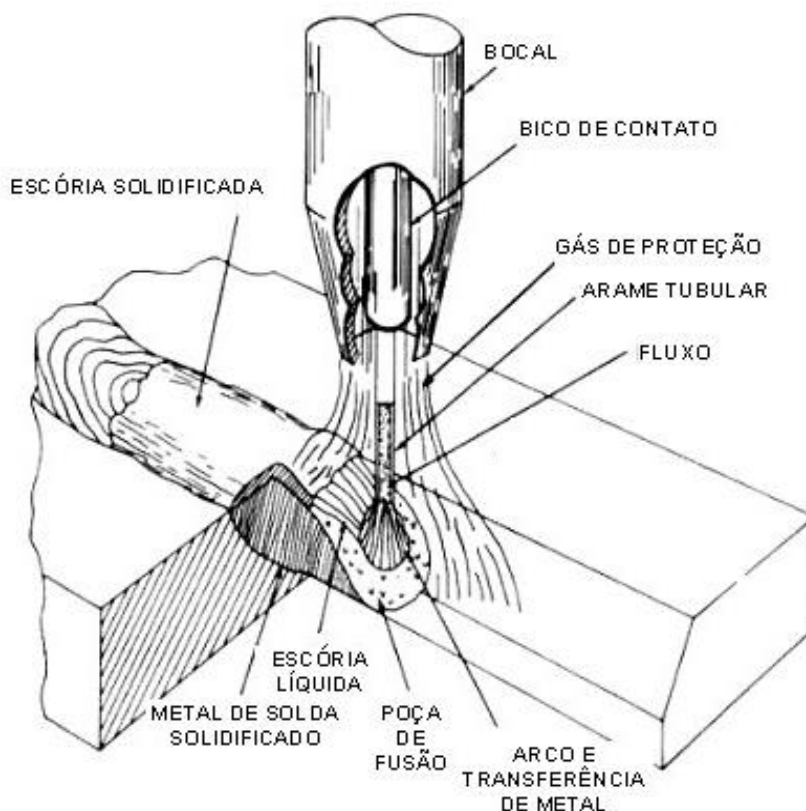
O processo de soldagem com arames tubulares com gás de proteção
